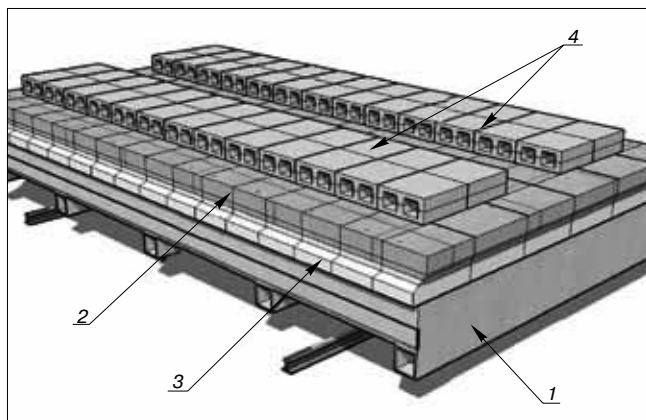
Конструкция печной вагонетки с использованием модульных блоков из жаростойкого бетона: 1 – основание печной вагонетки; 2 – окантовочные блоки верхнего ряда из жаростойкого бетона; 3 – окантовочные блоки нижнего ряда из жаростойкого бетона; 4 – элементы канализованного пода из жаростойкого бетона
